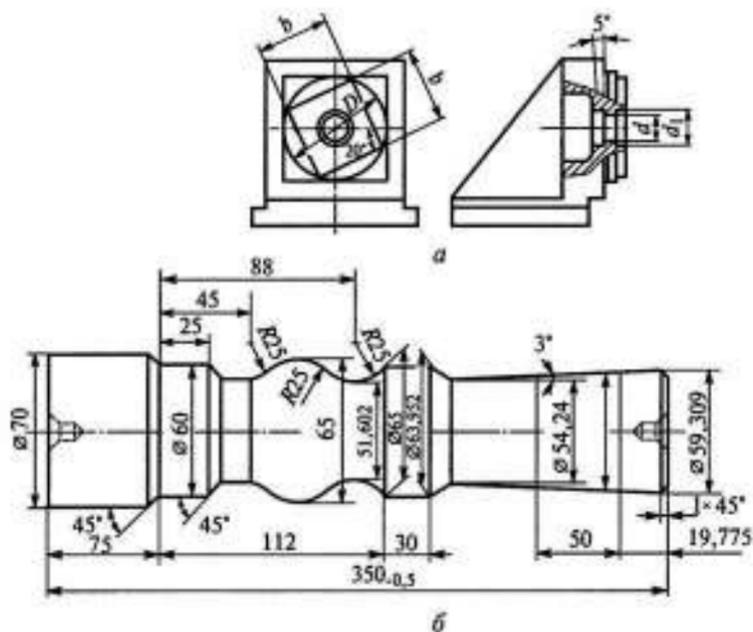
Чертеж эталона для комплексных испытаний многоцелевого станка с ЧПУ (а) и токарного станка с ЧПУ (б):
